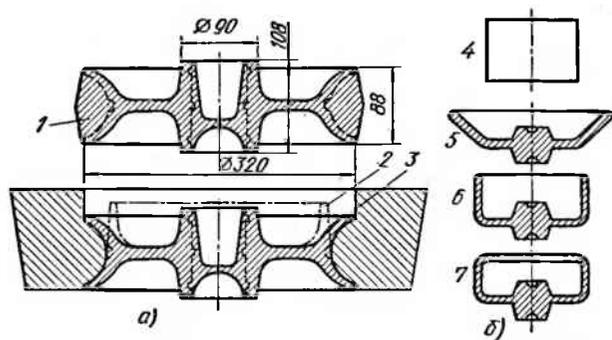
Переходы комбинированной штамповки при изготовлении:
